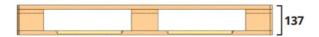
Esquema de vista lateral de um pallet com 137 mm de altura
